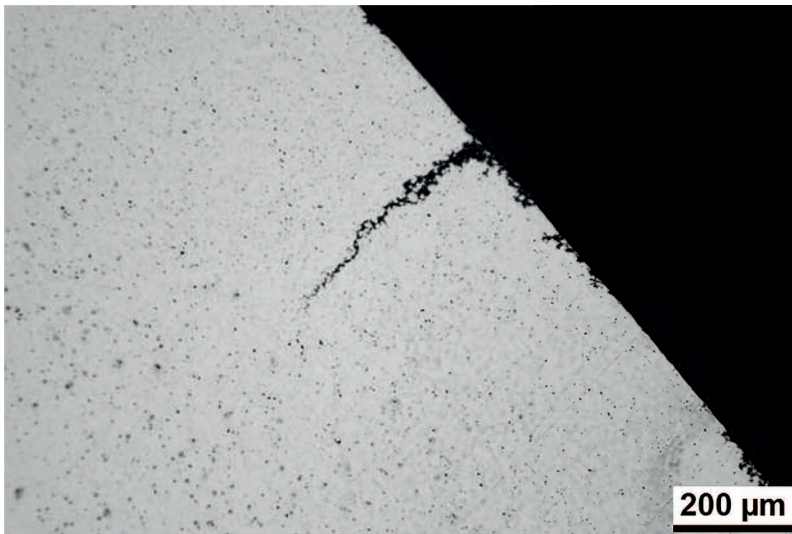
Dommages que la corrosion fissurante sous tension a causés sur une douille coulissante
